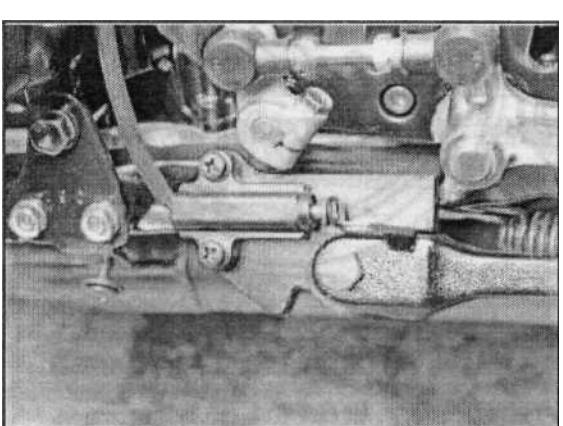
г Выключатель боковой подставки плунжерного типа
